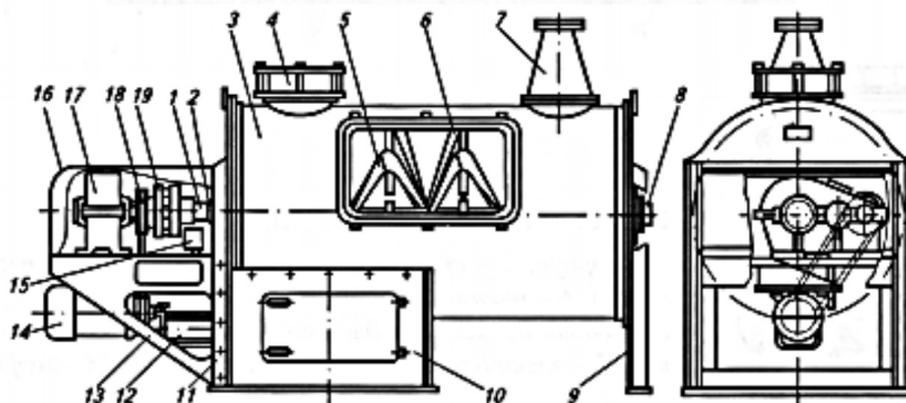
Горизонтальный смеситель А9-ДСГ-0,5: 1 – вал; 2, 8 – корпуса подшипников; 3 – корпус; 4, 7 – патрубки; 5, 6 – спиральные лопасти; 9, 11 – стойки; 10 – подсмесительный бункер; 12 – пневмоцилиндр; 13 – рама; 14 – электродвигатель; 15 – воздухораспределитель; 16 – ограждение; 17 – редуктор; 18 – клиноременная передача; 19 – муфта
